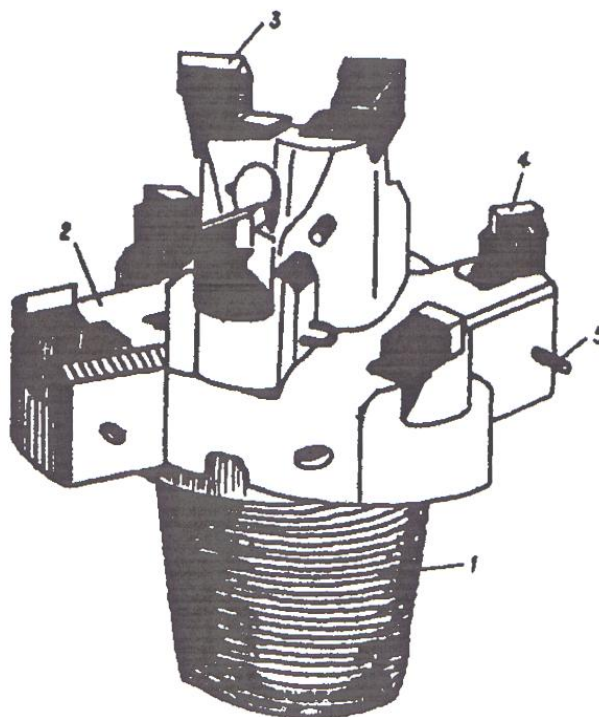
Режущий буровой инструмент ДР-160-244 конструкции НИИОГР: 1- ниппель; 2 – корпус; 3 – центральные резцы; 4 – боковые резцы; 5 – шплинт
